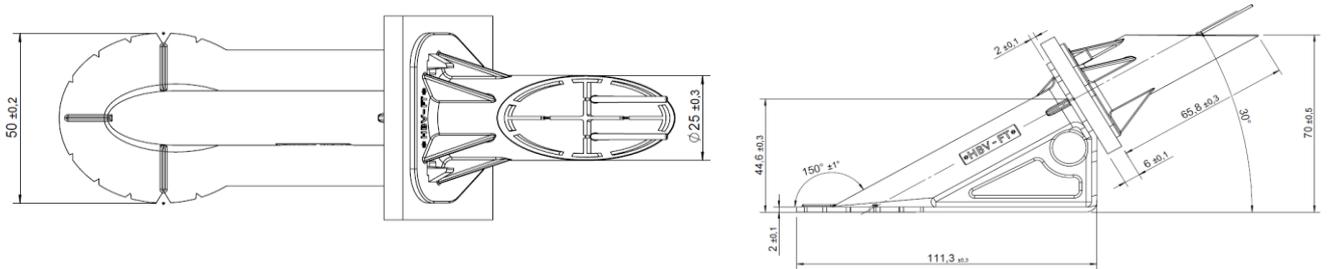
Draufsicht (links) und Seitenansicht (rechts) eines FT-Verbinders
